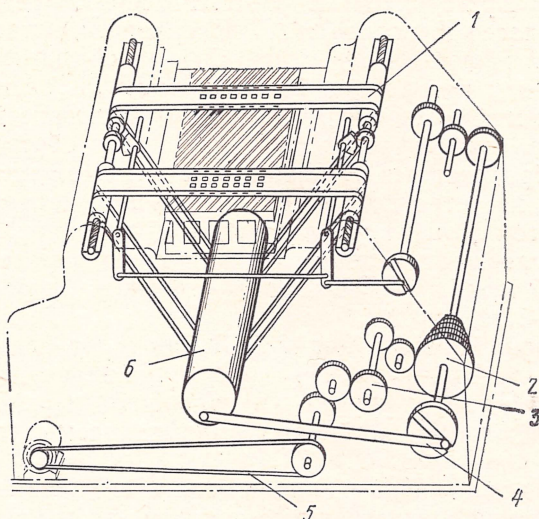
Кинематическая схема плоскопритирочного двухплитного станка конструкции Д. С. Семенова
